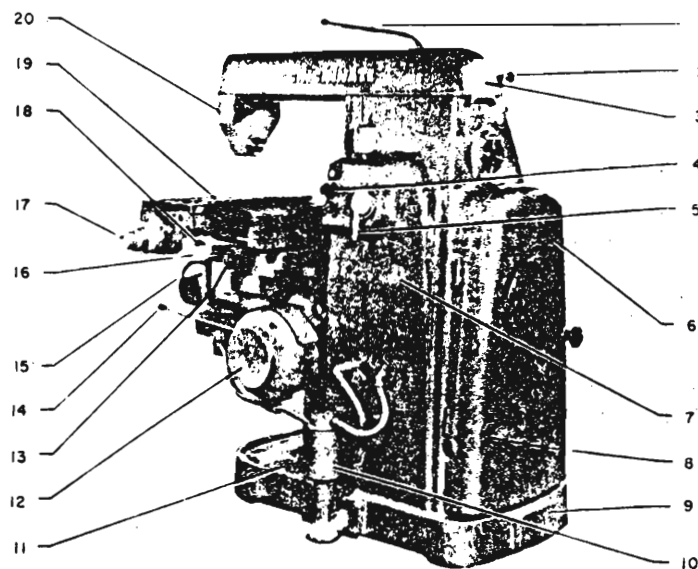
Nomenclatura de la fresadora corriente de columna y cartela, vista posterior (Cincinnati Milling Machine Co.)
